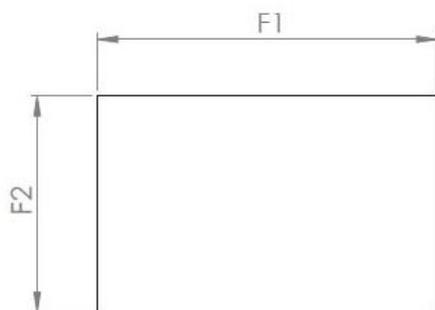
1.1.1 Rectángulo soporte peldaño. Dimensionado previo.
